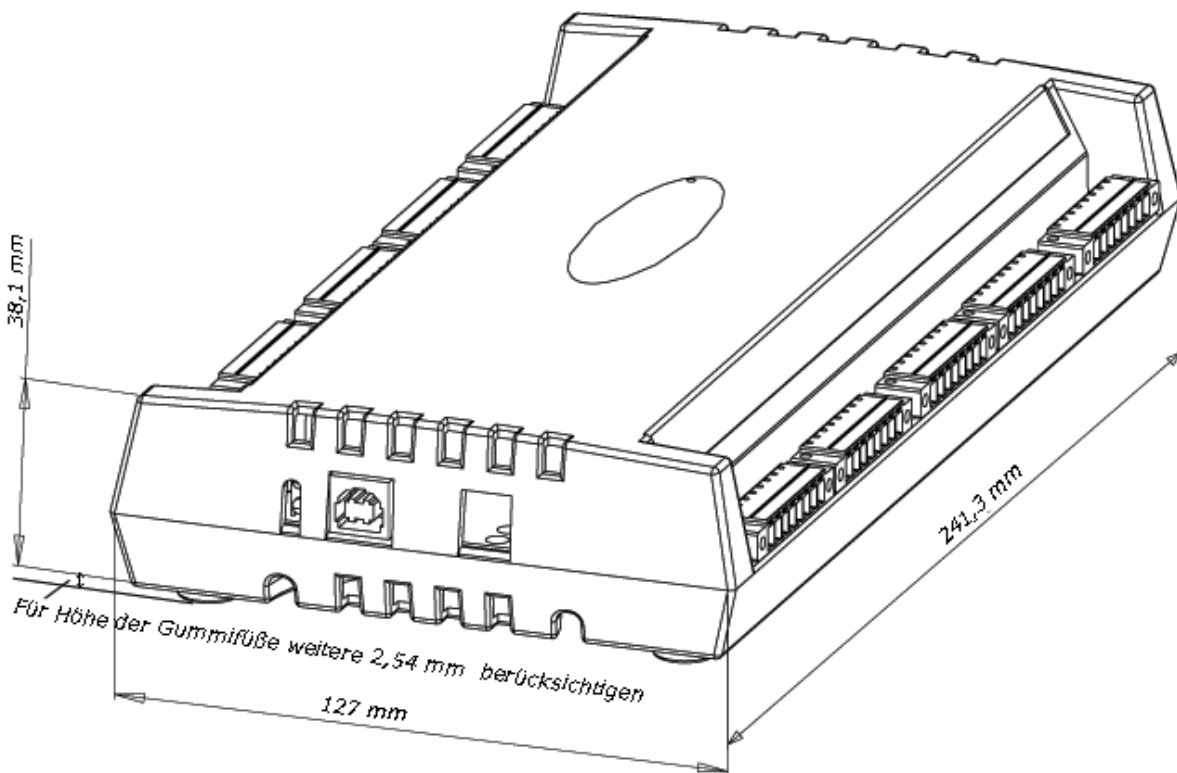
Gehäuseabmessungen des RedLab 2416-4AO
